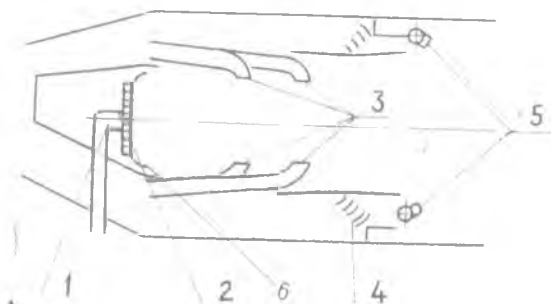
Форсажная камера II контура: 1 — форсунка; 2 — фронтное устройство; 3 — патрубки для воздуха; 4 — генераторы вихрей; 5 — форсунки дополнительного впрыска; 6 — стабилизатор
